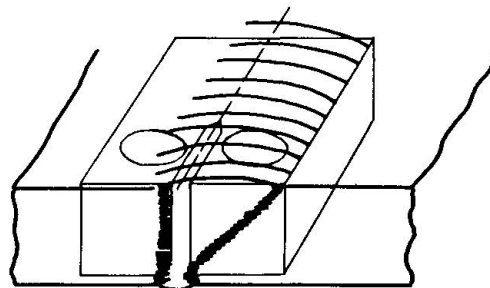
Prélèvement des éprouvettes dans les joints soudés bout à bout
